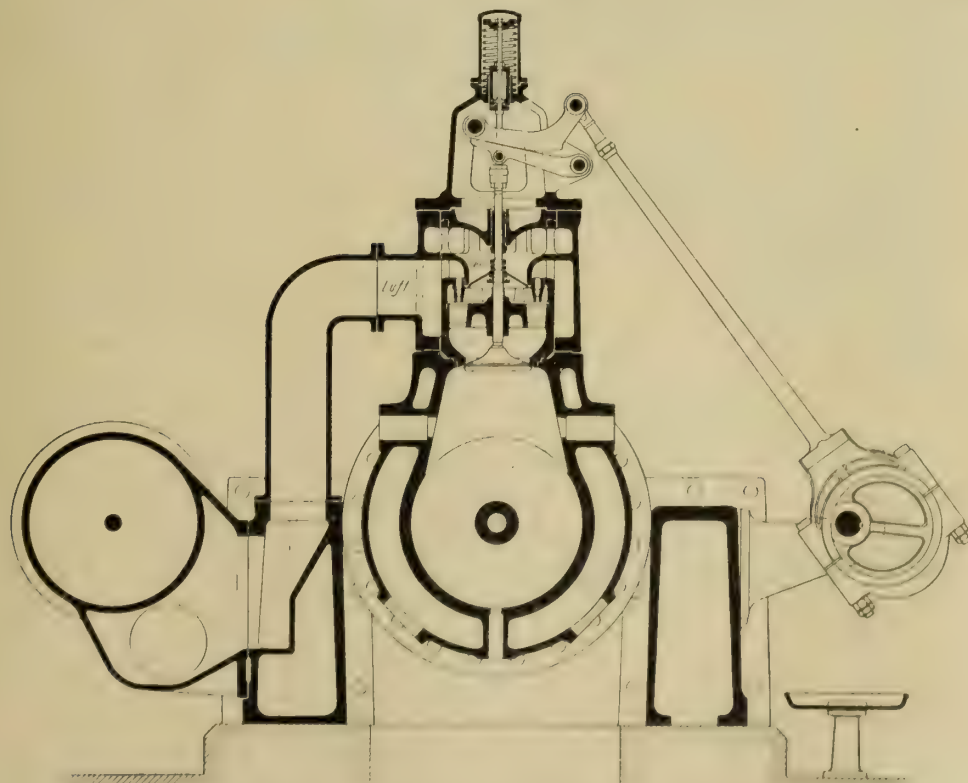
Querschnitt durch Einlaßventil und Steuerung der Gasmachine.
